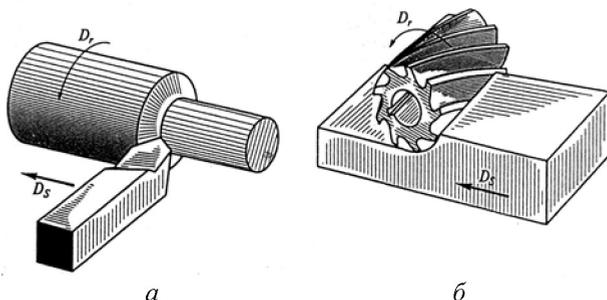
Схемы процесса резания для точения (а) и фрезерования (б):
